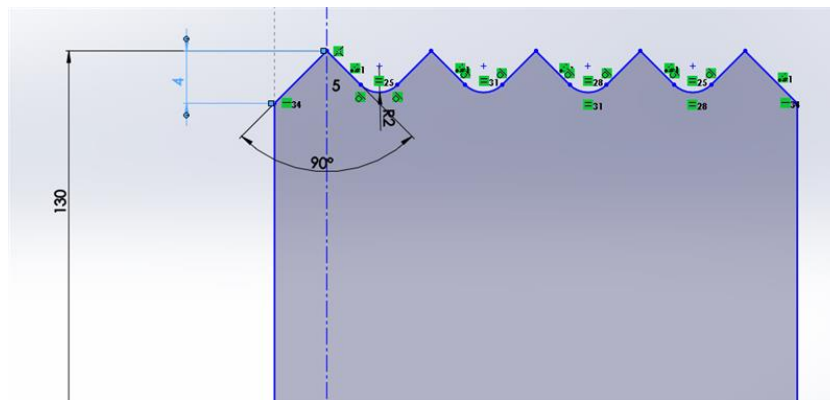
Dettaglio sul disegno realizzato su solidworks del trigger da 90° usato come riferimento per la fresa a CNC
